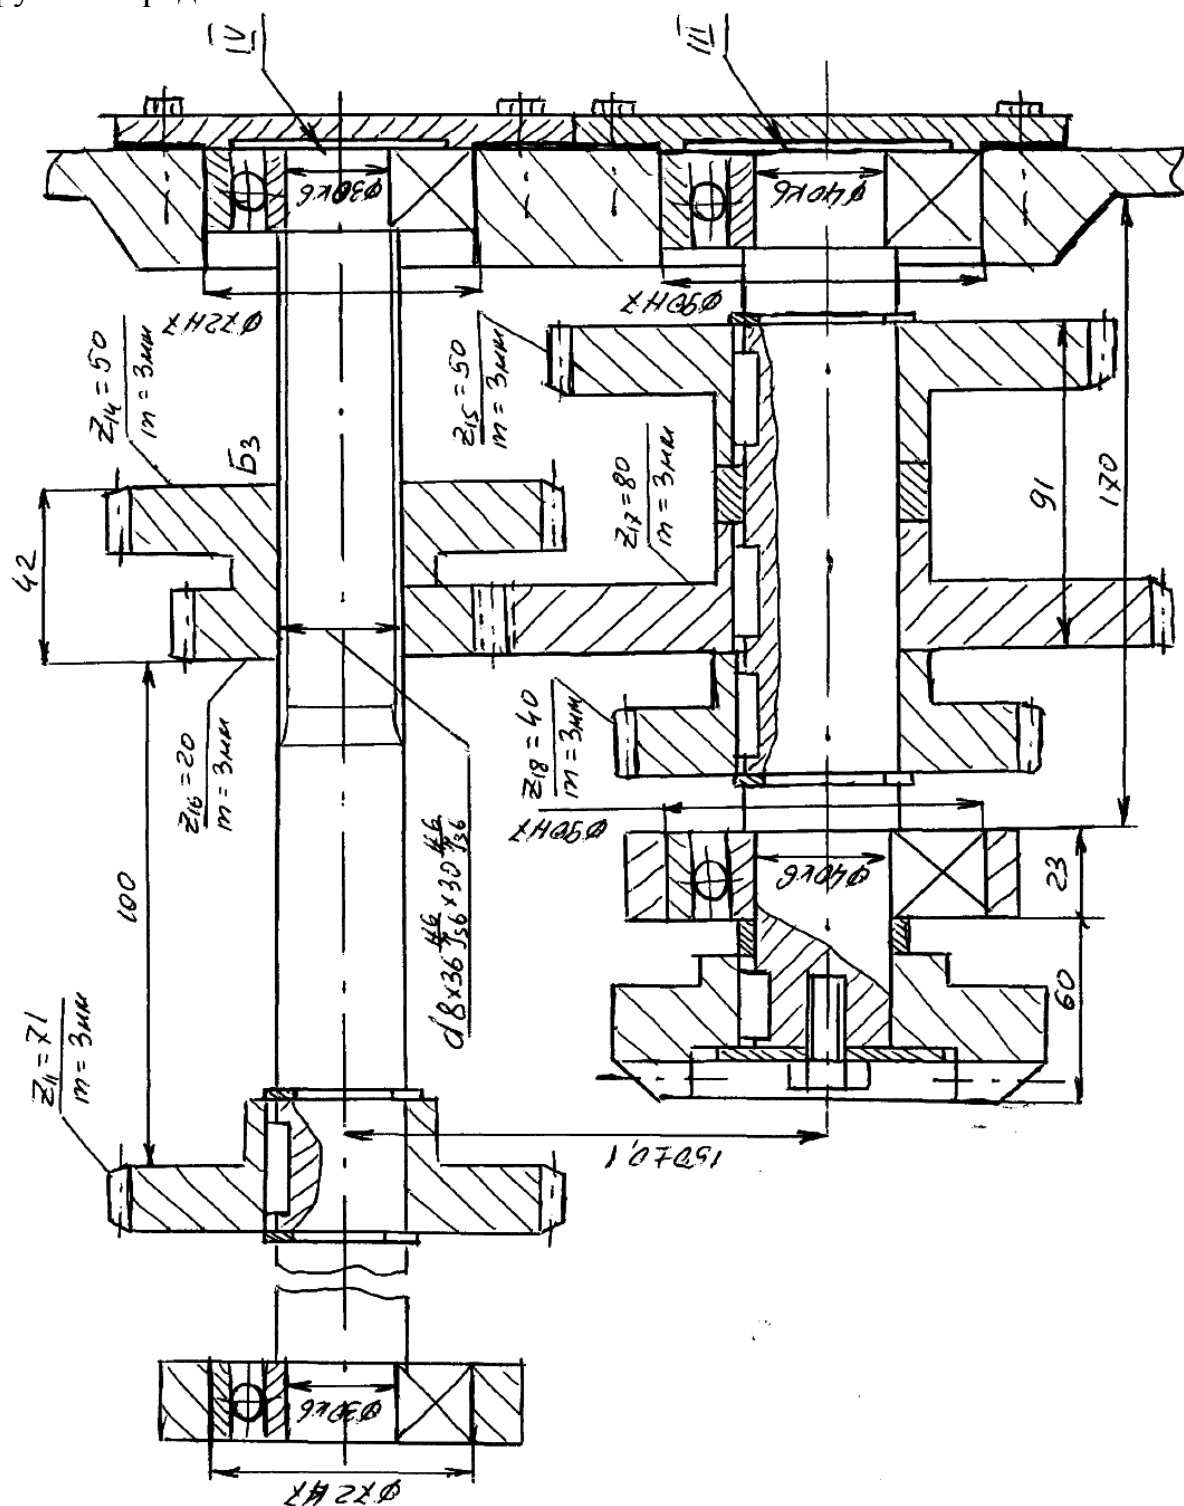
Сборочный чертеж наиболее нагруженной группы передач
